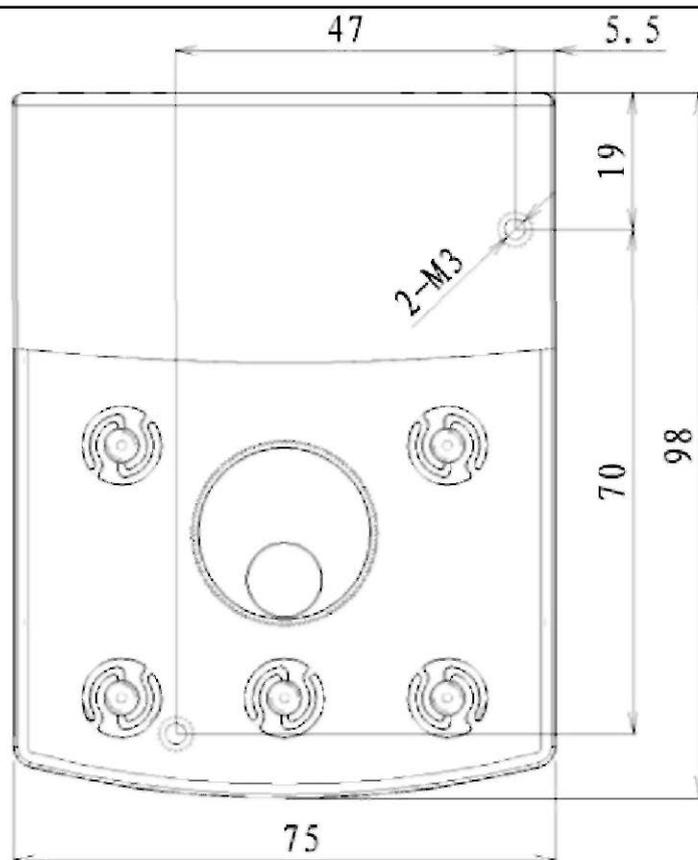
Чертеж клавиатуры и размеры отверстий
